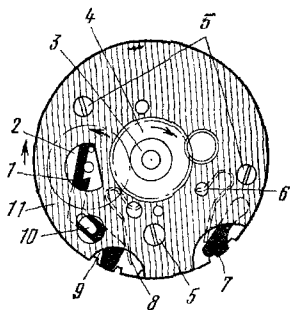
Схема расположения деталей календарного устройства часов «Луч» 1816:
